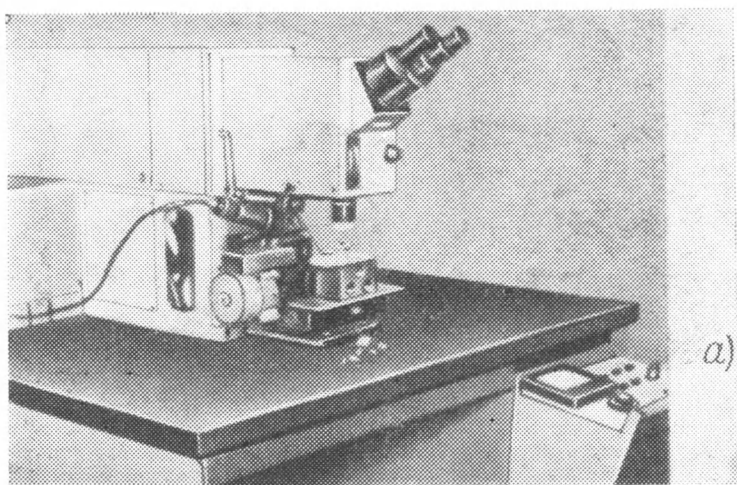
Установка для лазерной сварки «Квант-12»:
